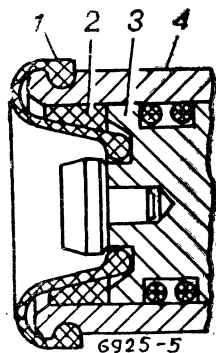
Установка пенополиуретановых колец в колесные цилиндры:
